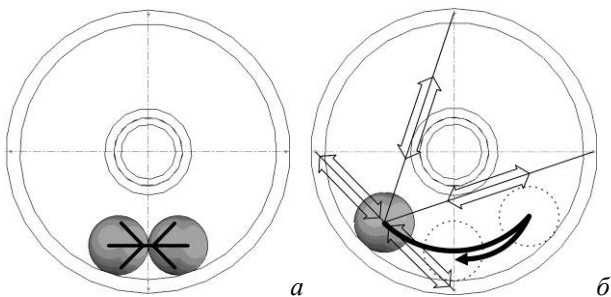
Встановлення куль у корпус АБ: а – встановлений тривимірний контакт двох куль; б – з'єднання кулі з 4 демпферами
